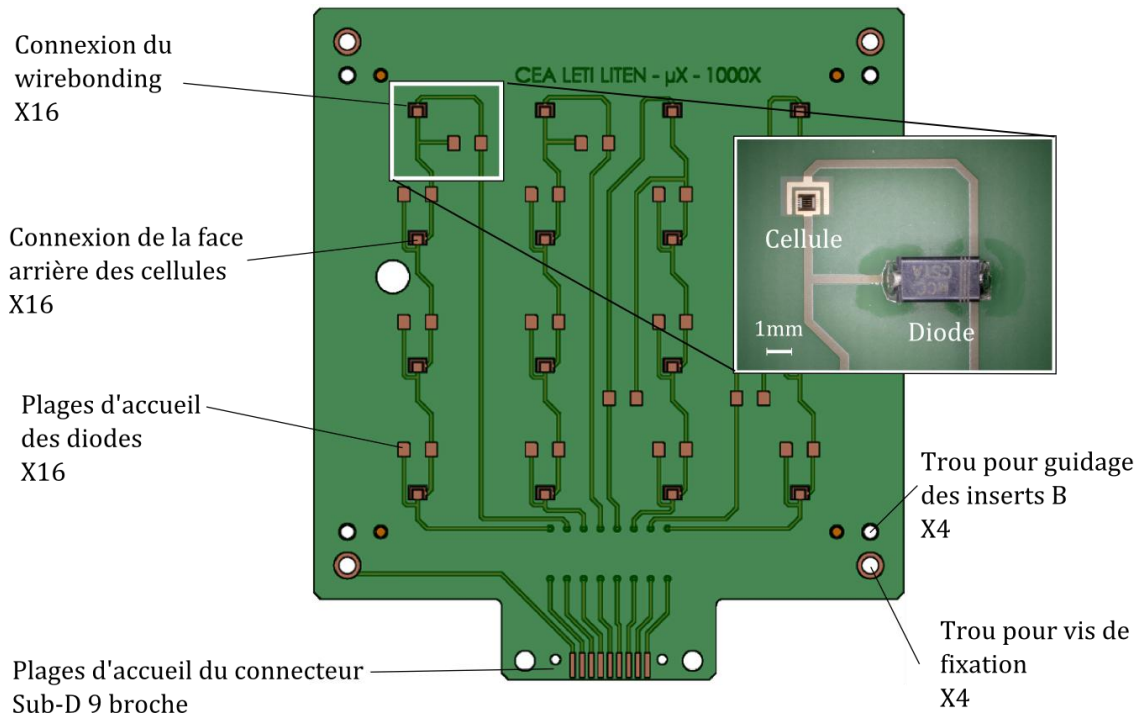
Dessin CAO du PCB (Printed Circuit Board)
